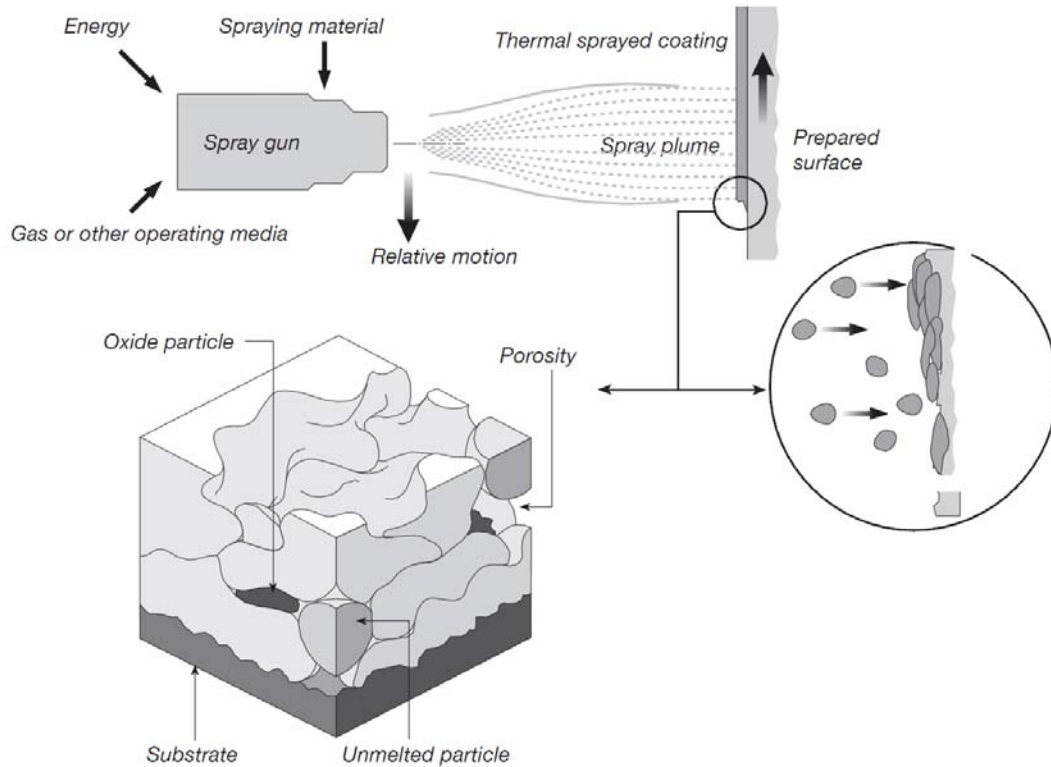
Principe du dépôt par projection thermique [Sulzer 11]
